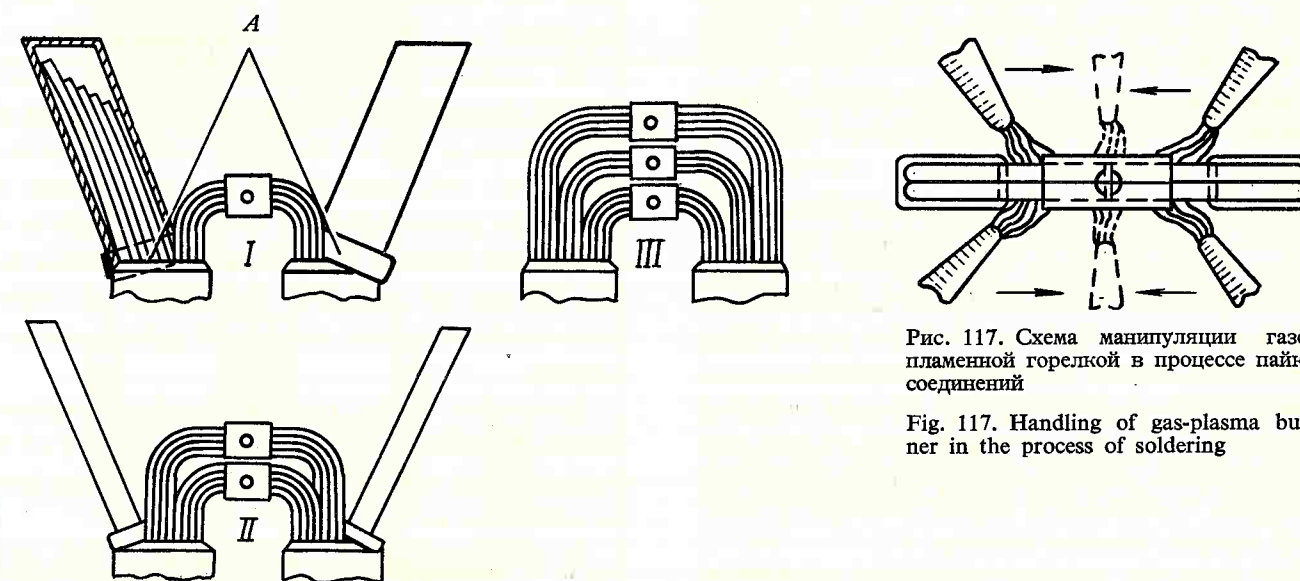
Этапы сборки и пайки головок обмотки статора, состоящих из трех ветвей:
